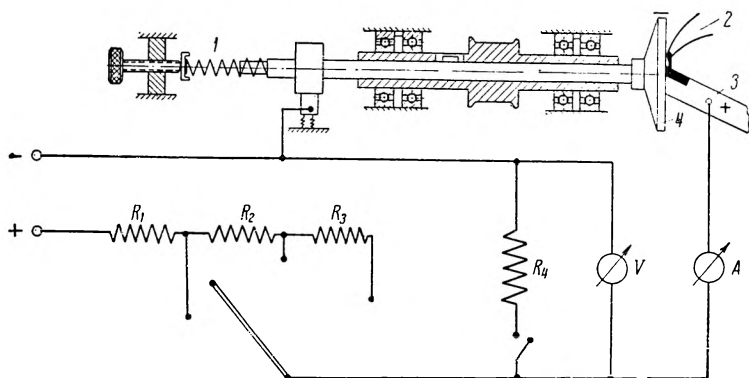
Схема станка для анодно-механической заточки режущего инструмента
